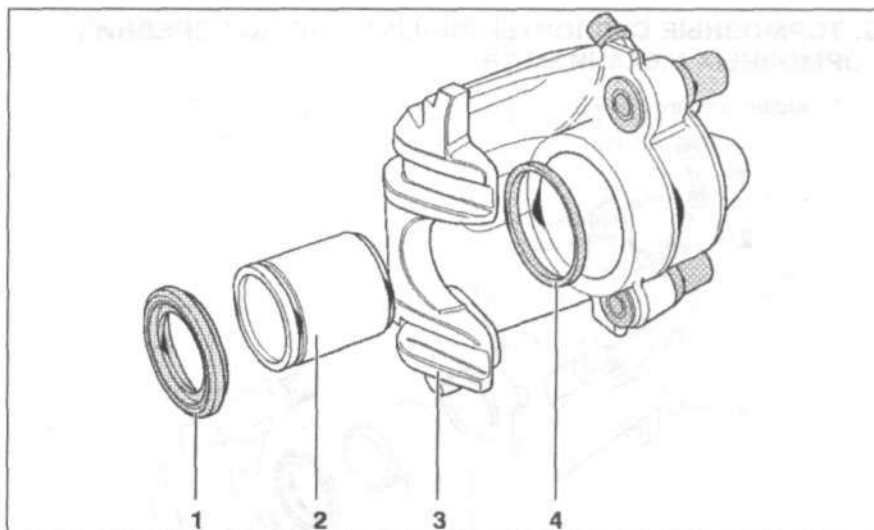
Тормозные суппорты «VW I» и «VW II»: 1, 4 – Сальники; 2 – Поршень; 3 – Корпус тормозного суппорта.
